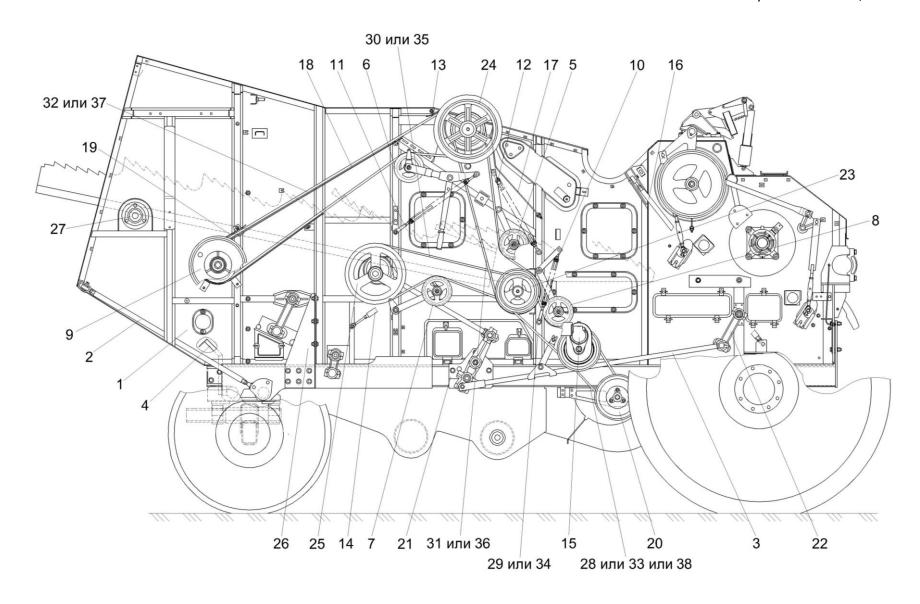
Очистка КВК-8А-0202000-02 (вид справа)
